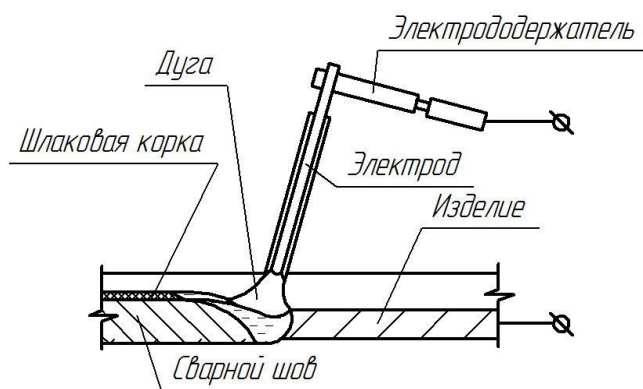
Схема ручной дуговой сварки штучными электродами
